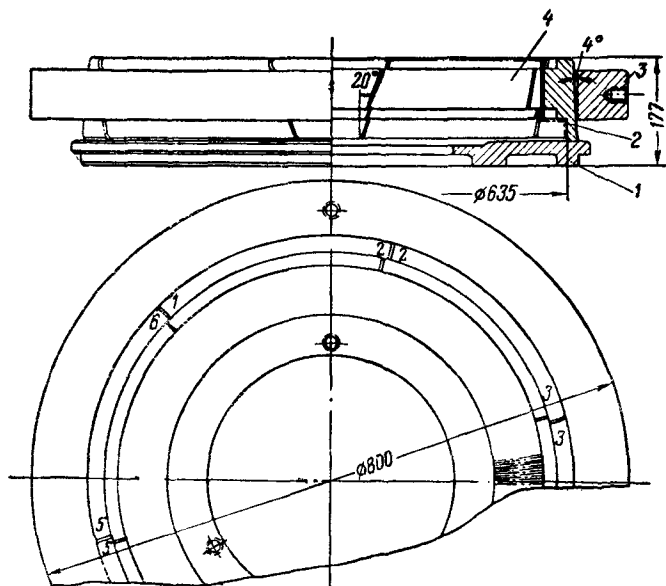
Приспособление для опрессовки пластин коллектора тягового двигателя ДПЭ-340:
